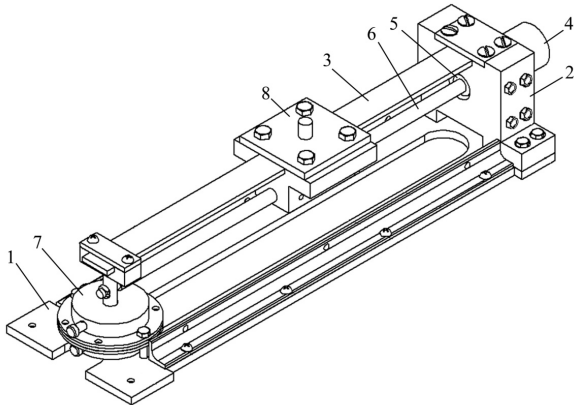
Динамический виброгаситель колебаний: 1) основание; 2) корпус; 3) упругий элемент; 4) шаговый двигатель; 5) шаровая опора; 6) ходовой винт; 7) пневматический демпфер; 8) подвижная масса со встроенной гайкой качения
